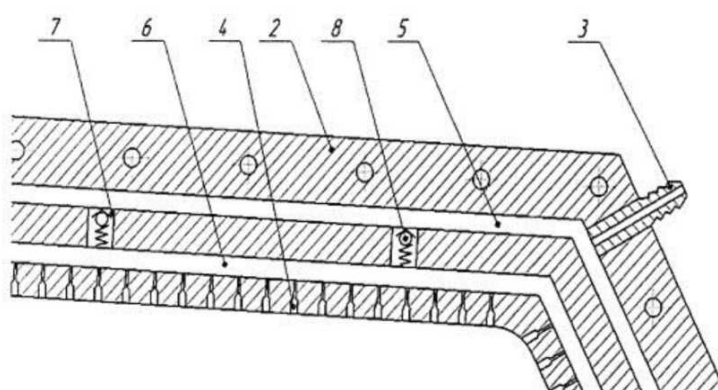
Продольный разреза крышки кристаллизатора: 1 – корпус кристаллизатора; 2 – крышка кристаллизатора; 3 – впускной патрубков устройства подачи смазки; 4 – выходные отверстия; 5 – проточка со стороны внешнего контура крышки; 6 – проточка со стороны внутреннего контура крышки; 7 – соединительные каналы; 8 – обратные клапаны [90, 104].
